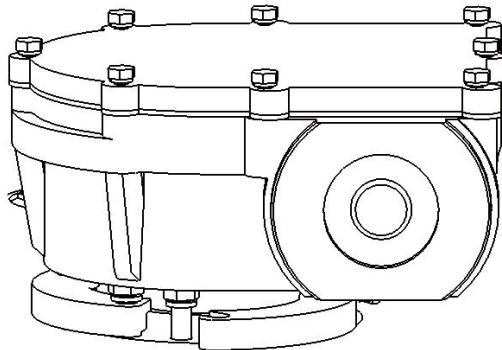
Откручивание крепежных пластин верхнего редуктора
